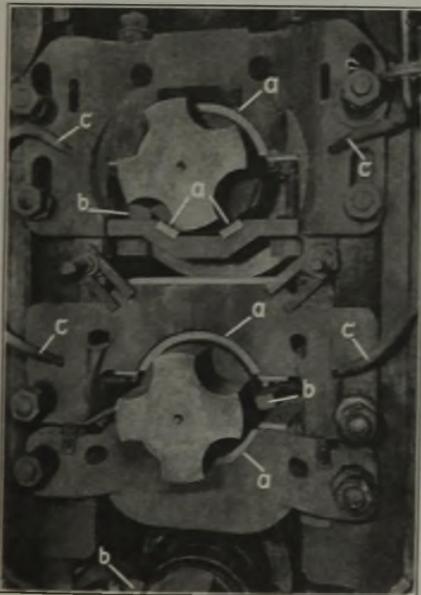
Mit Kunstharz ausgefütterte Einbaustücke einer Trio-Profilstahlstraße, betriebsmäßig im Walzenstand eingebaut. Ansicht gegen die Stirnseite.
